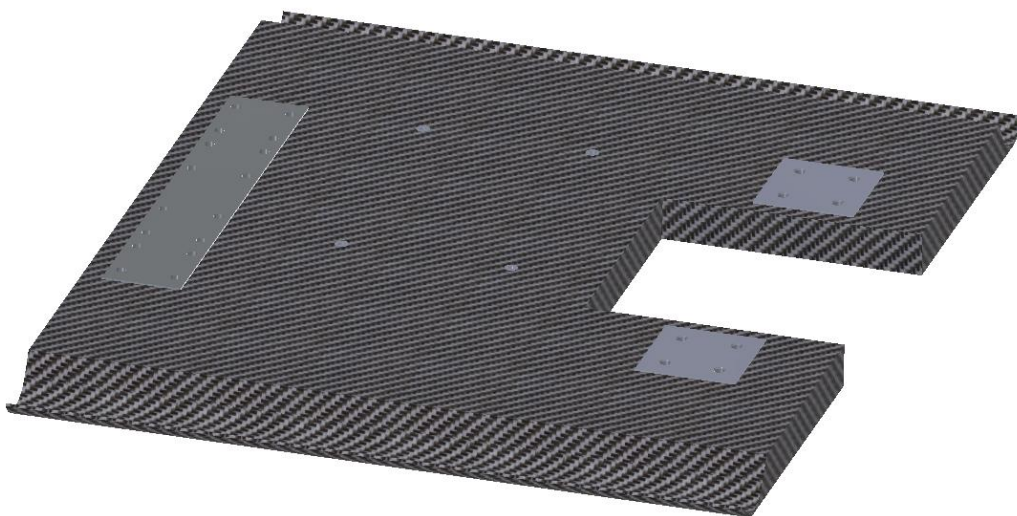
Modelo CAD, vista inferior de la plancha central.
